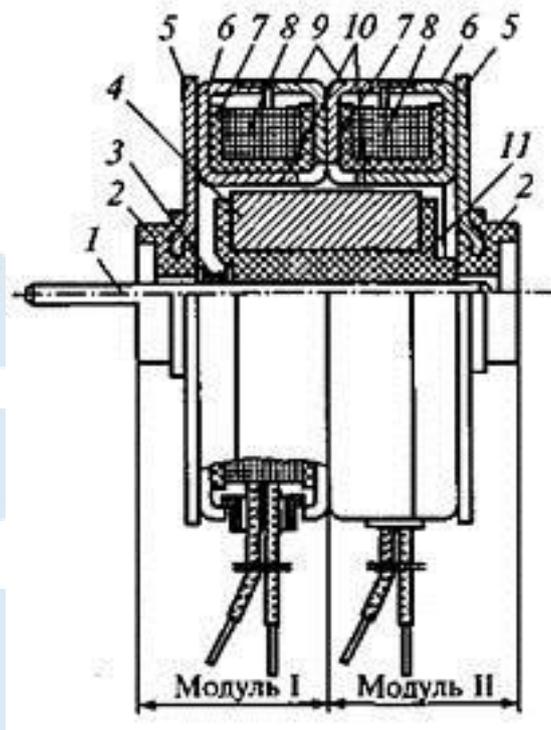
Конденсаторный многополюсный двигатель ДСК-32-0,25-0,375:
